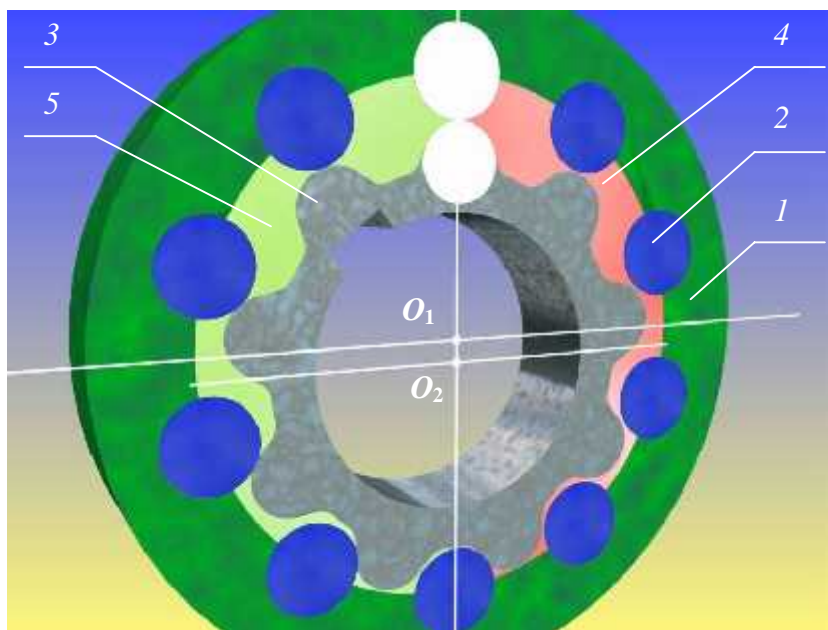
Героторное движение вытеснителей: 1 – охватывающий вытеснитель; 2 – ролики; 3 – охватываемый вытеснитель; 4 – зона нагнетания; 5 – зона слива.
